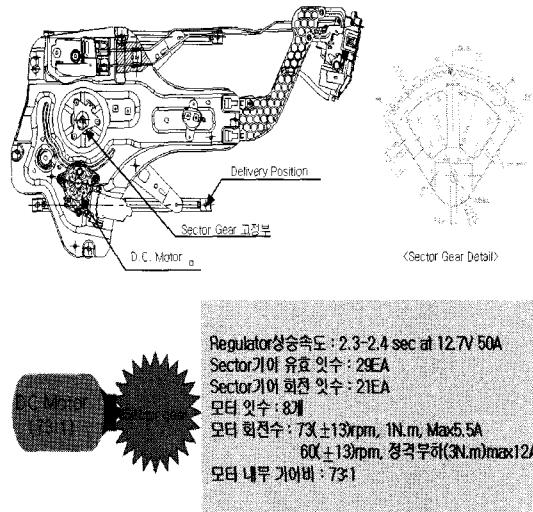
Window Regulator Module 의 개략도와 Sector Gear의 특성
